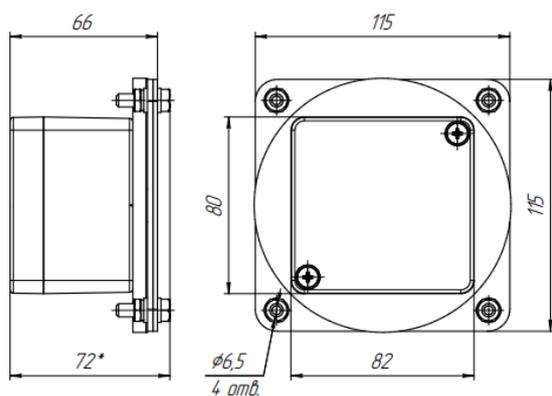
Габаритные и присоединительные размеры. СУМ-1П (пластиковый корпус)
